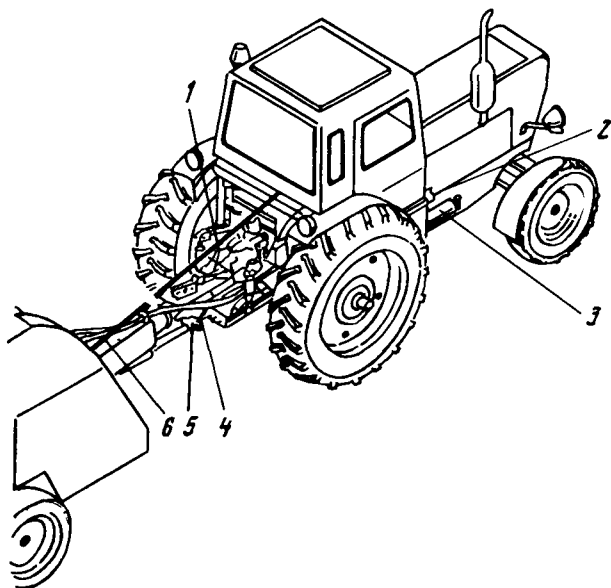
Присоединение пресс-подборщика ПР-Ф-750 к трактору: 1 - цепь фиксации кожуха; 2 - щипцы; 3 - рукоав L = 2010 мм; 4 - прицепная вилка; 5 - серьга; 6 - шнур
